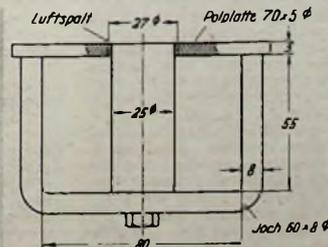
Eisenkörper eines 4-Watt-Lautsprechers
